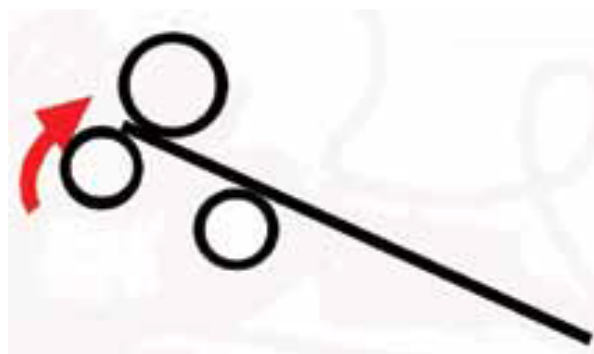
Montaje de la chapa en la máquina de 3 rodillos
